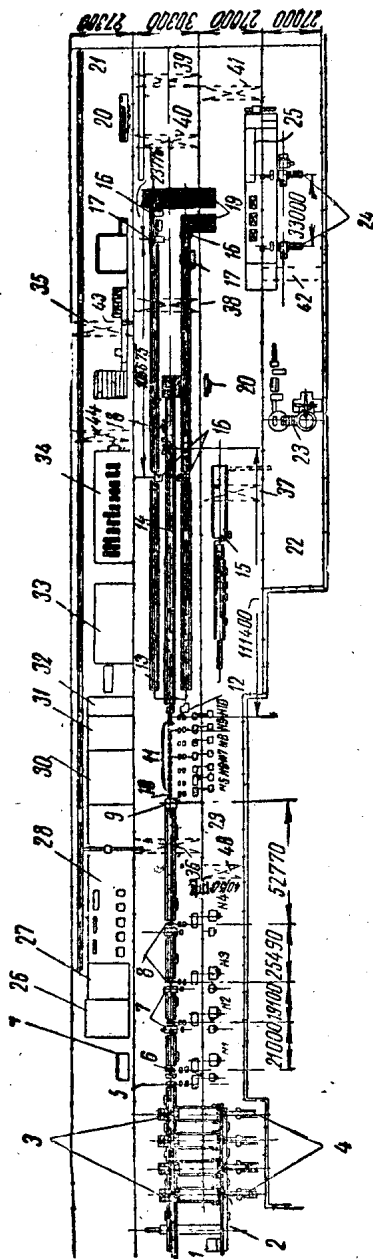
1680 公厘連續式鋼板軋机的設備布置平面图
